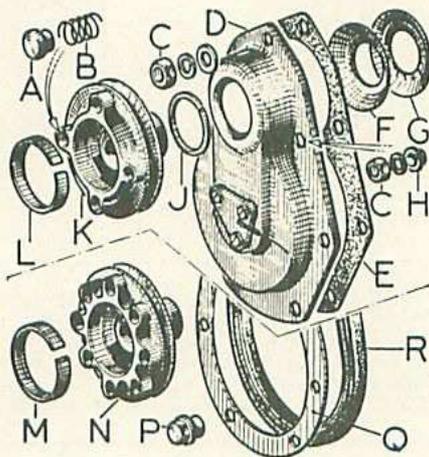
Détail du montage de la poulie et du couvre-engrenage
